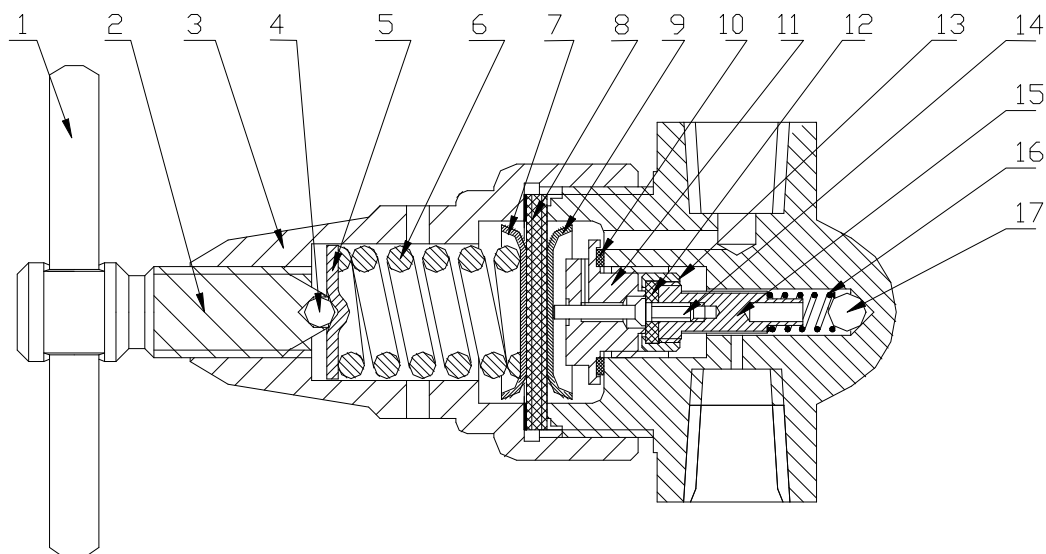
减压阀组件结构图 Structure diagram of pressure reduction valve assembly
